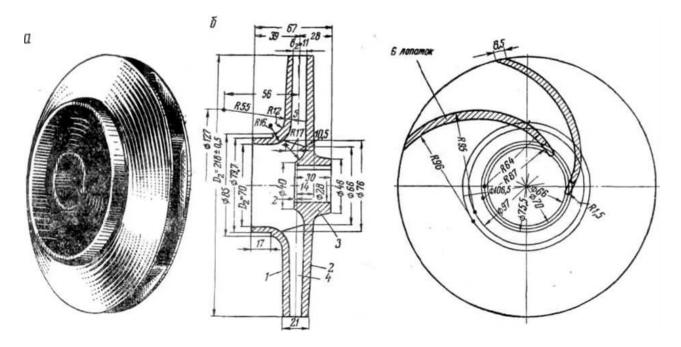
Рабочее колесо насоса типа К: a — общий вид; б — чертеж рабочего колеса насоса К 90/55; 1 — передний диск; 2 — задний диск; 3 — ступица; 4 — лопатки
